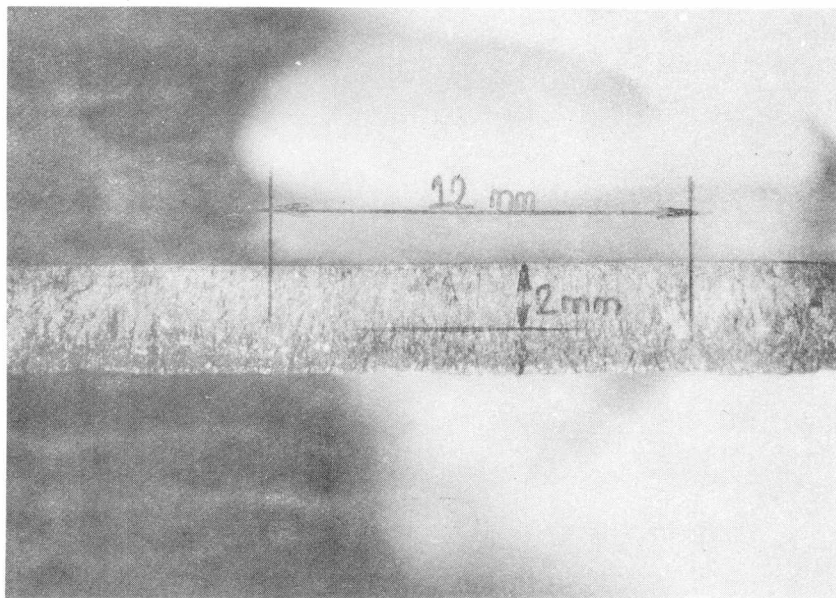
Detalle de la zona de iniciación de la fisura.
